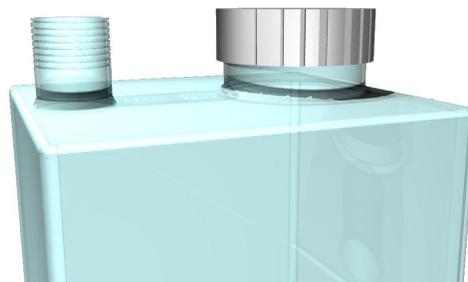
Tapa de la boca de llenado aplicada al tanque
